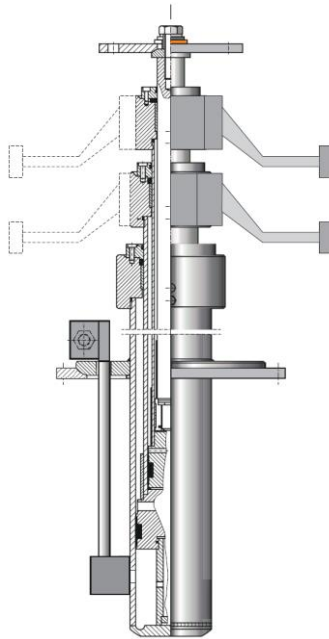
Cilindro telescopico con schema indicativo attacchi e bracci di guida
